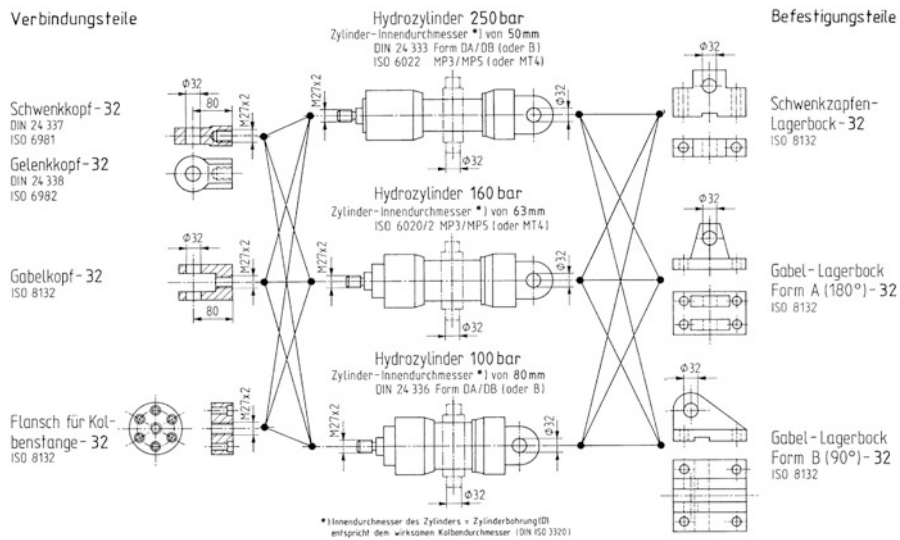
Differenzialzylinder in Rundbauform mit Befestigung durch Schwenk-/Gelenkauge hinten (oder Drehzapfenbefestigung) für Nenndruckstufen (PN) und größengestuft nach Zylinder-Innendurchmesser (D) (Normzylinder; ZBD 1001, 1601, 2502, Storz Fluidtechnik) kombiniert mit Anbauteilen gleicher Type (genormte Anbauteile; KS, KG, RC, RF bzw. TB, CBA, CBB, Storz) nach Weisser [448]
